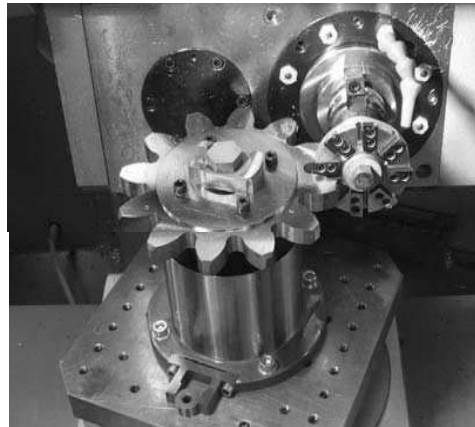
Нарізання зубчастого колеса на горизонтальному фрезерному верстаті з ЧПК за методом контурного оброблення
